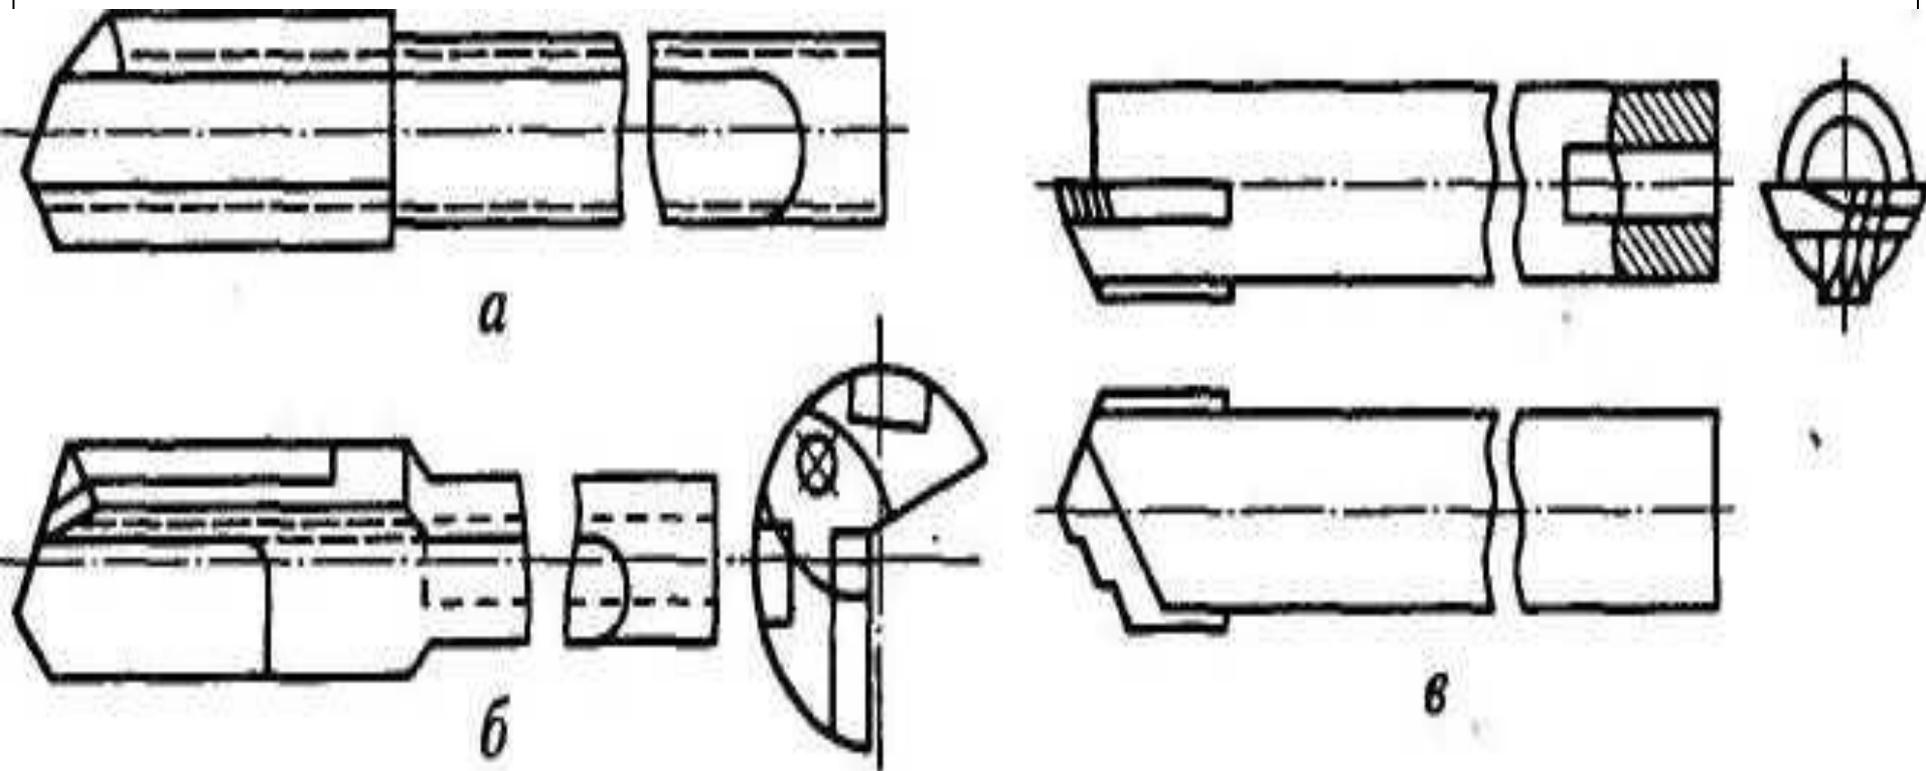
Ружейные сверла: а - с колоском из быстрорежущей стали; б - армированное пластинами из твердого сплава; в - с внутренним отводом СОЖ
